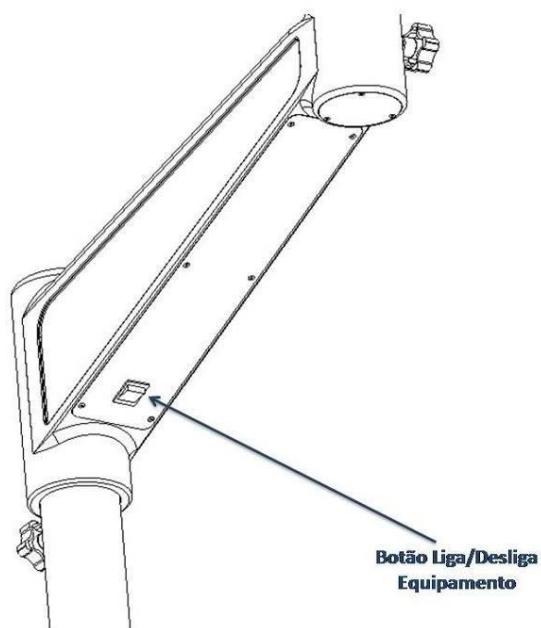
Ilustração do braço fixo indicando o botão Liga/Desliga equipamento.
